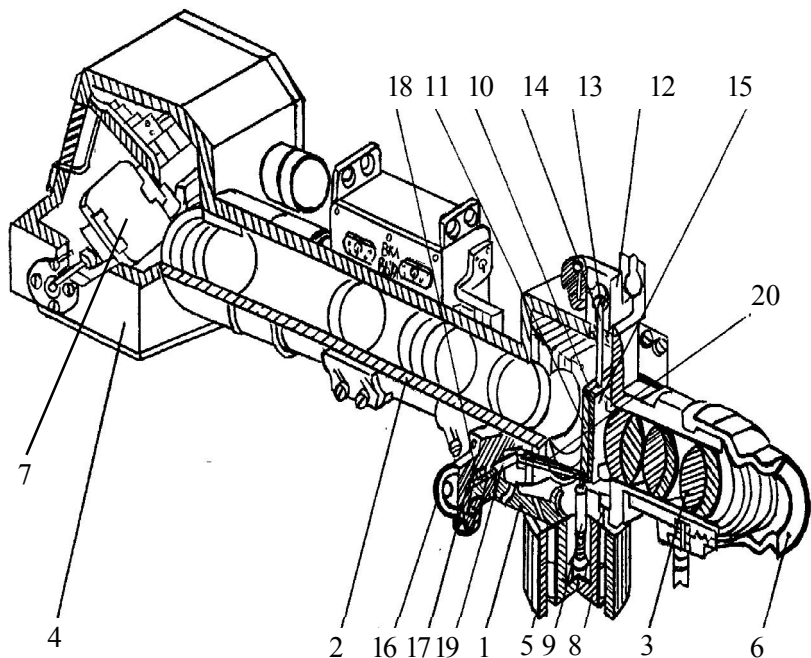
Телескопічний оптичний приціл ОП 5-38: 1 – корпус; 2 – труба; 3 – окулярна частина; 4 – головка; 5 – маховик; 6 – захисний ковпачок окуляра; 7 – дзеркало; 8 – гайка; 9 – гвинт; 10 – каретка; 11 – сітка; 12 – корпус з кришкою; 13 – гайка; 14 – гвинт; 15 – каретка з ниткою; 16 – корпус; 17 – маховик з черв'яком; 18 – черв'ячне колесо з гвинтовою нарізкою; 19 – гвинт; 20 – повзун
